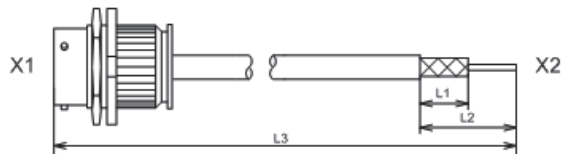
Заготовка кабельной сборки, оснащённая панельным соединителем с одной стороны
